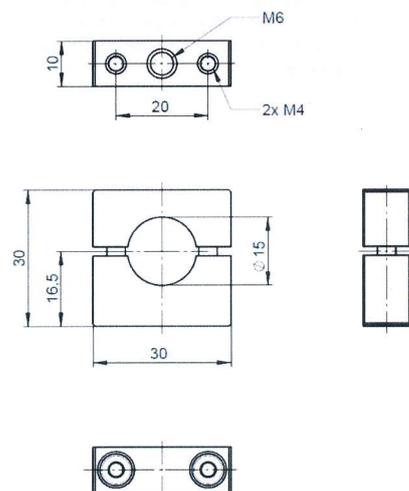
Support B2-LD, plan coté (mesures en mm)
